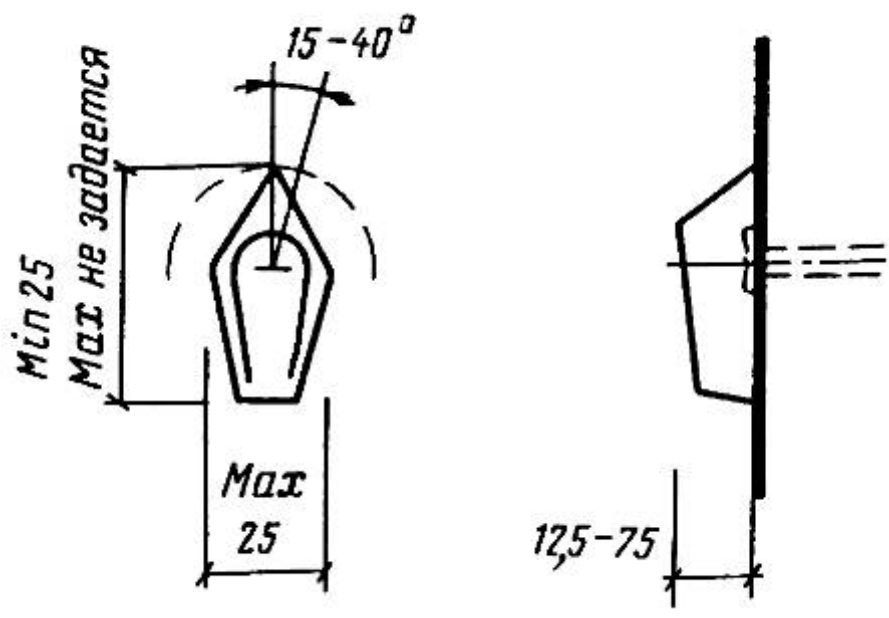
Форма ручек для ступенчатого поворота меньше чем на 360° (размеры в мм)
